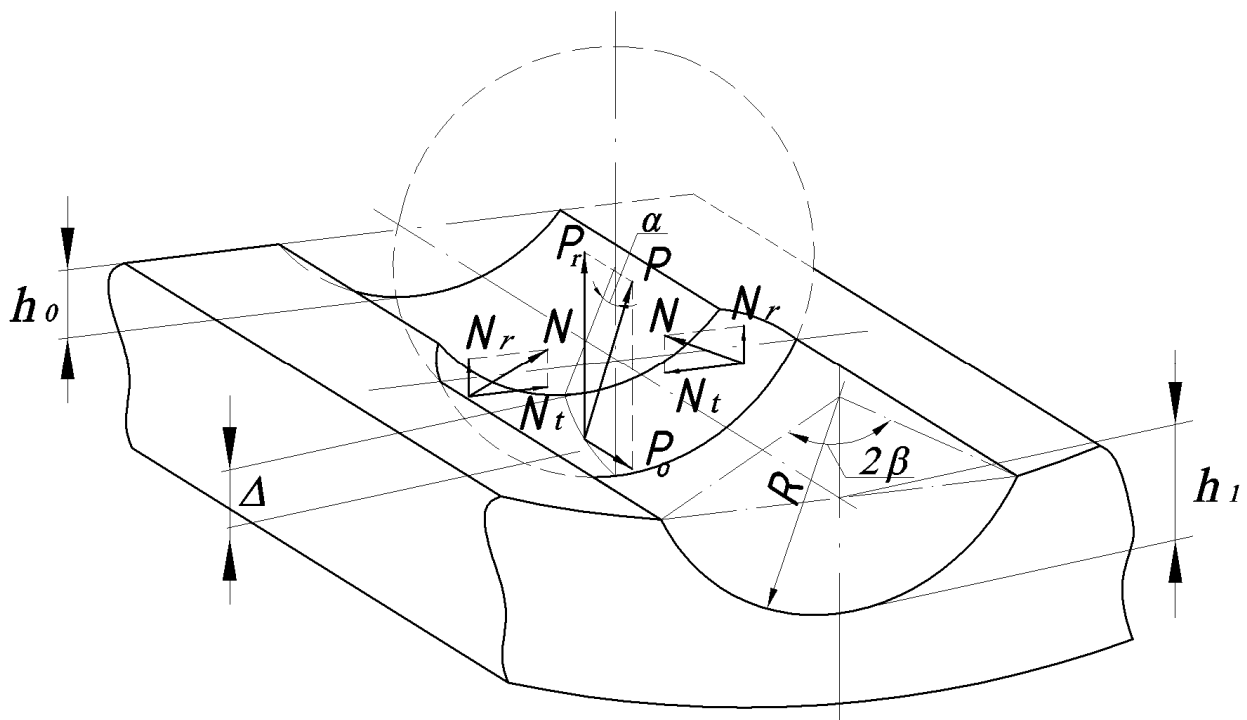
Розрахункова схема дії сил при обробленні півкруглої шліцевої канавки
